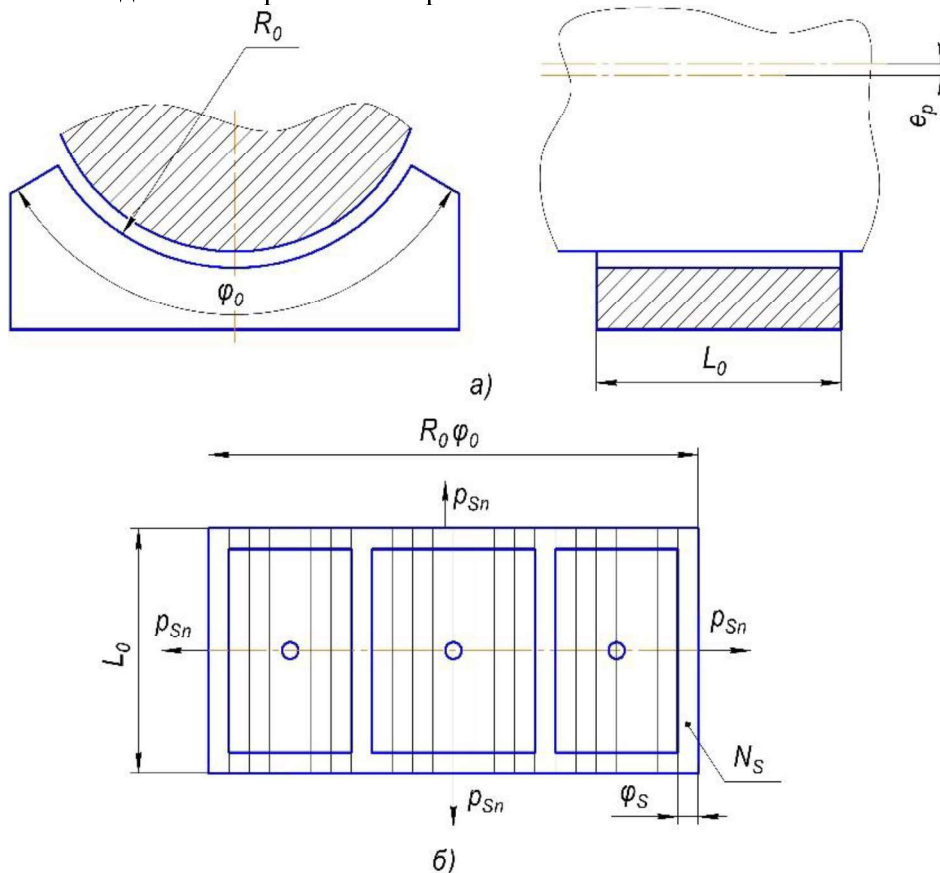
Гидростатический подшипник с неполным углом обхвата: а) расчетная схема; б) развертка опорной поверхности
